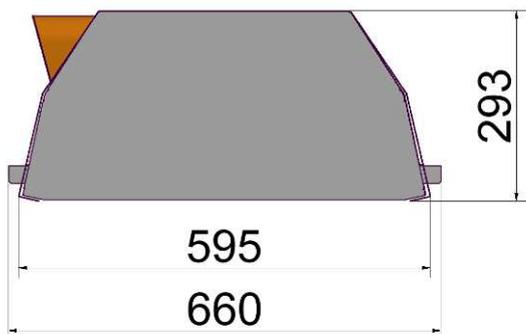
Dimensiones de deltaSchwank 950U
